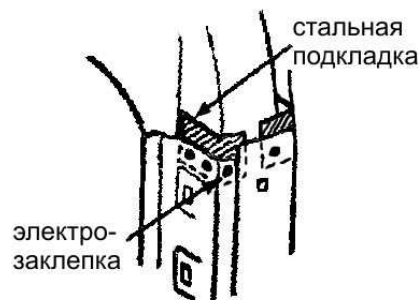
Сварка с подкладной стальной неудаляемой пластиной
